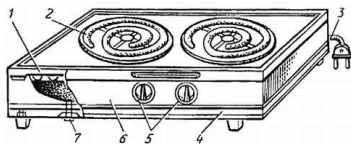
Электроплита «Мечта»: 1 — верхняя крышка; 2 — нагревательный элемент; 3 — шнур с вилкой; 4 — нижняя крышка; 5 — переключатели мощности; 6 — корпус; 7 — винт.
